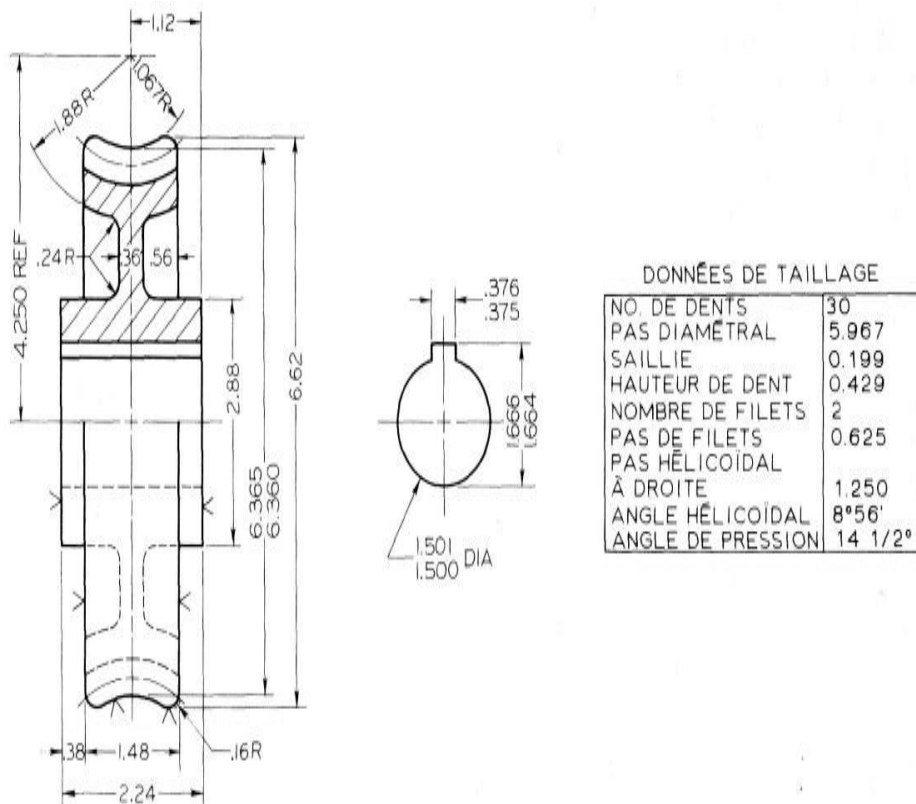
Dessin de fabrication d'une roue d'engrenage à vis
